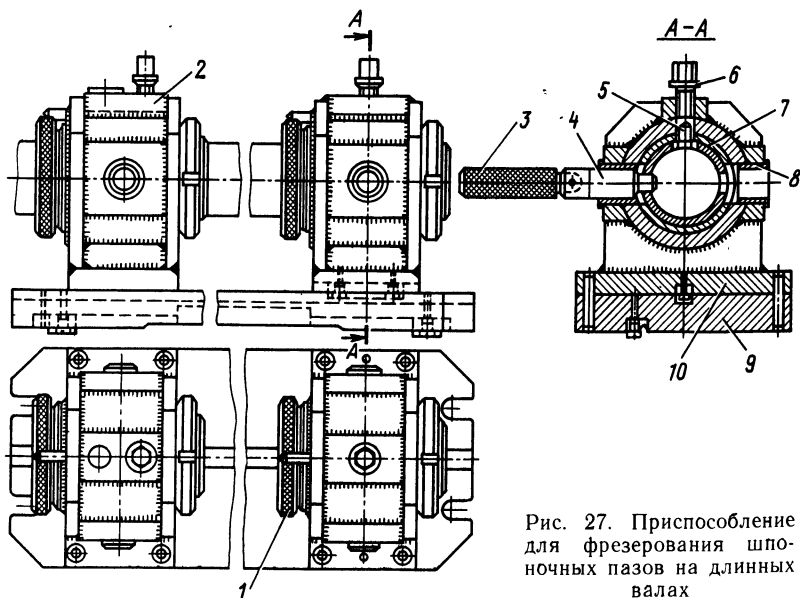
Приспособление для фрезерования шпоночных пазов на длинных валах
